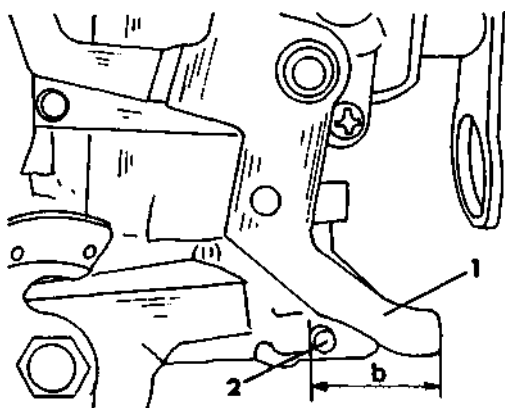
Seřizovačí šroub sytiče -1-u karburátorů Solex
